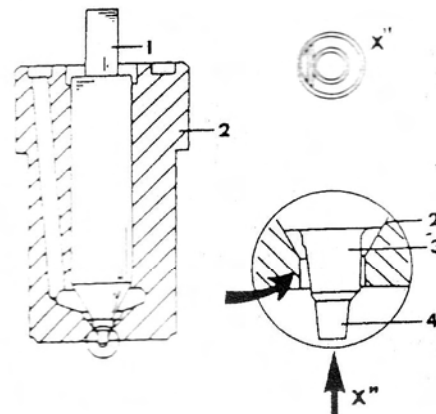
Установка форсунки на пятицилиндровых двигателях.
